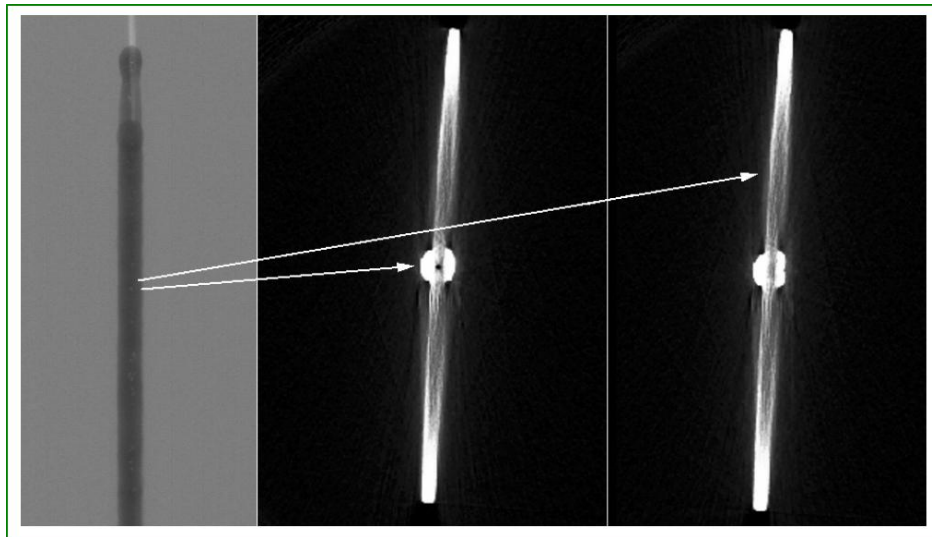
Imagen radiográfica de soldadura a) radiografía frontal, b) y c) cortes de las secciones señaladas donde se pueden observar poros.^[26]
